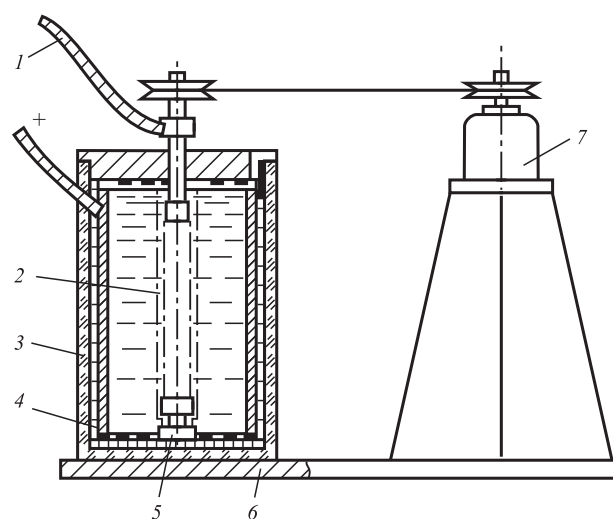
Установка для покрытия наружных поверхностей цилиндрических деталей:
